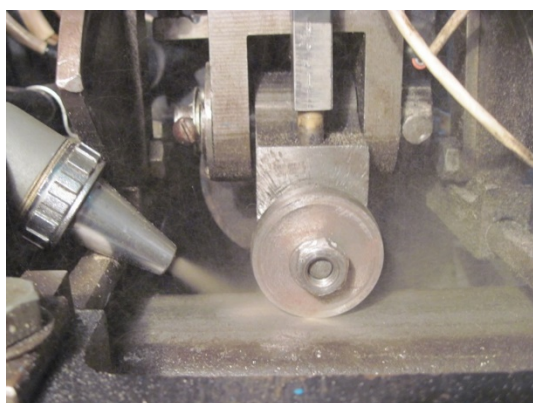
Струминно-абразивний вплив на контакт робочих поверхонь
